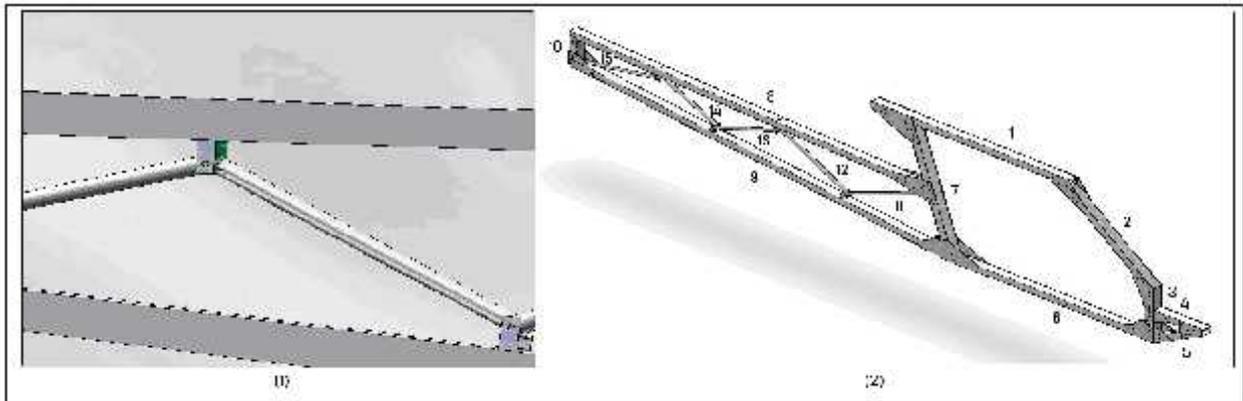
Le châssis obtenu après assemblage et un zoom sur la partie queue
